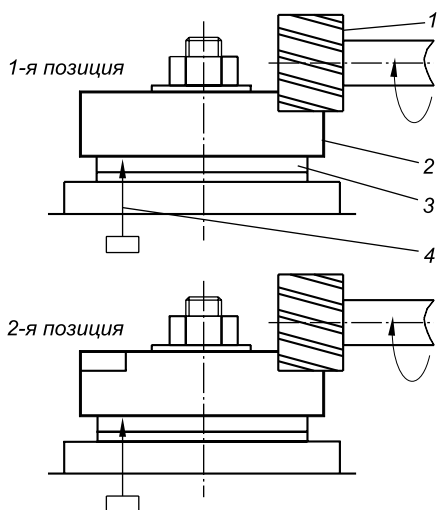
Схема фрезерной обработки уступов заготовки:
